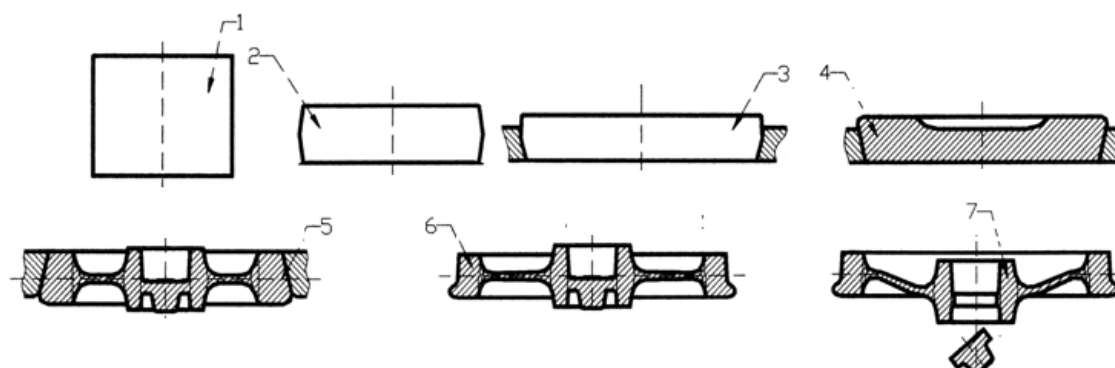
Технологическая схема деформирования колесной заготовки: 1 – исходная заготовка, 2 – предварительная осадка, 3 – осадка в технологическом кольце, 4– разгонка металла пуансоном, 5 – формовка заготовки, 6 – раскатка колеса по диаметру, 7 – выгибка диска, калибровка обода, прошивка отверстия и клеймение
